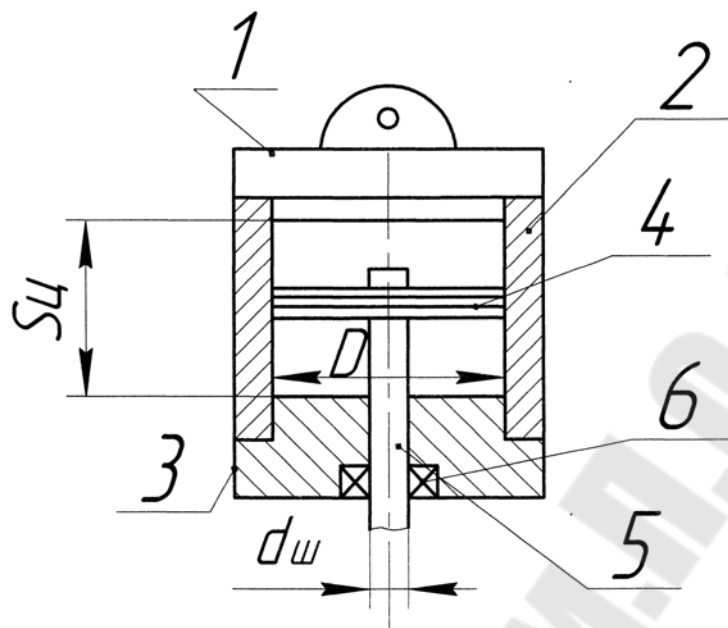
1 – верхняя крышка; 2 – цилиндр (гильза); 3 – нижняя крышка; 4 – поршень; 5 – шток; 6 – уплотнение.
